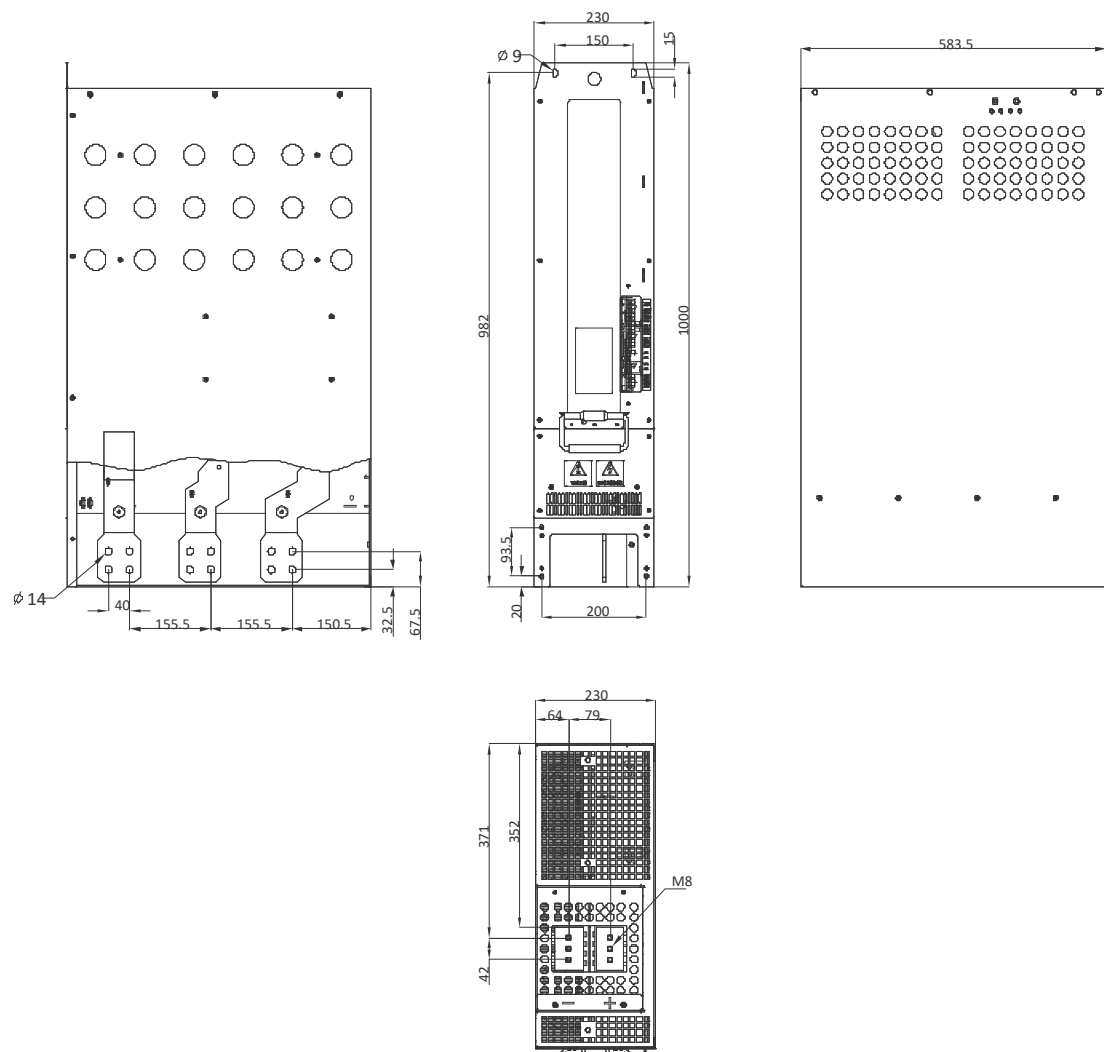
Габаритные размеры инвертора корпуса FR8I (мм)
